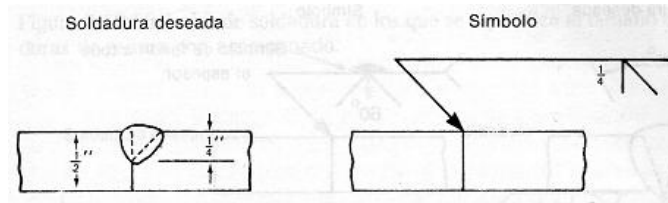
Símbolo de soldadura en el que se especifica la profundidad de la soldadura de ranura.
